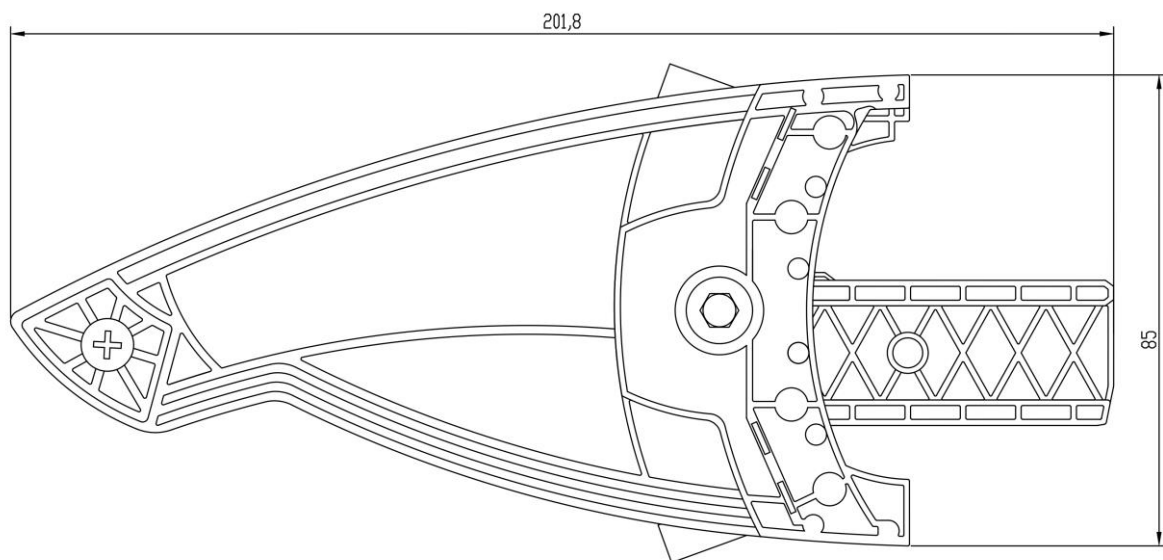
Общий вид тестовой крышки ЭПТК. Вид сбоку.
